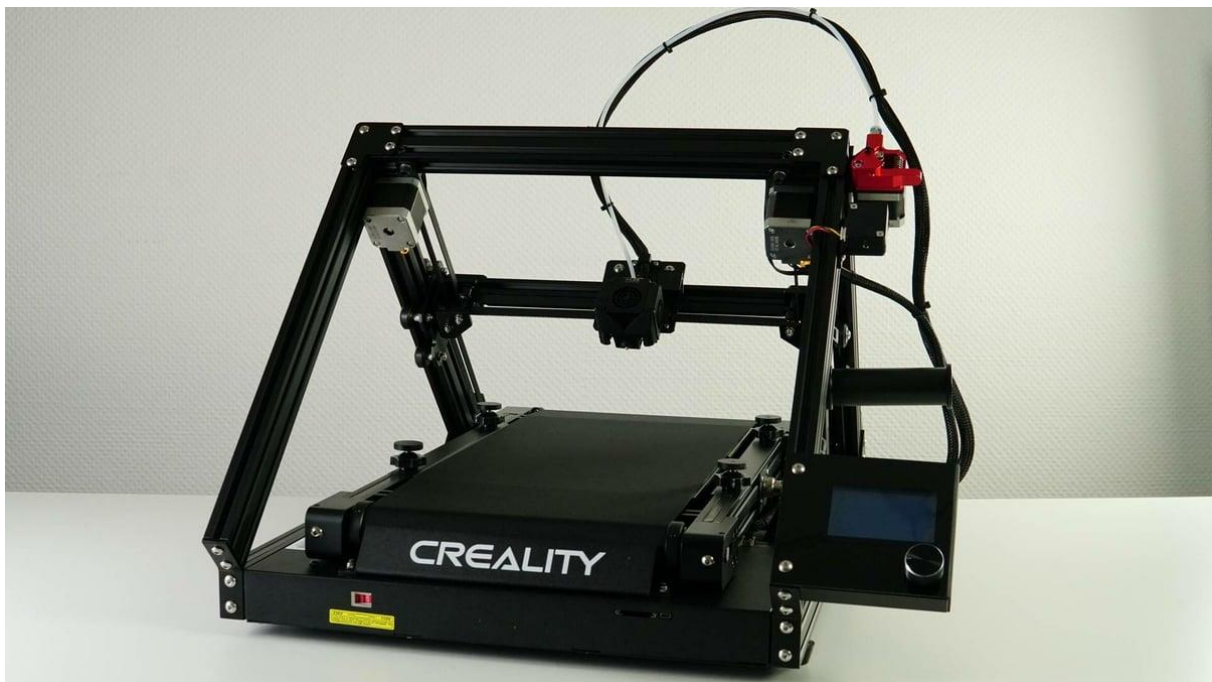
Стрічковий FDM 3D-принтер
